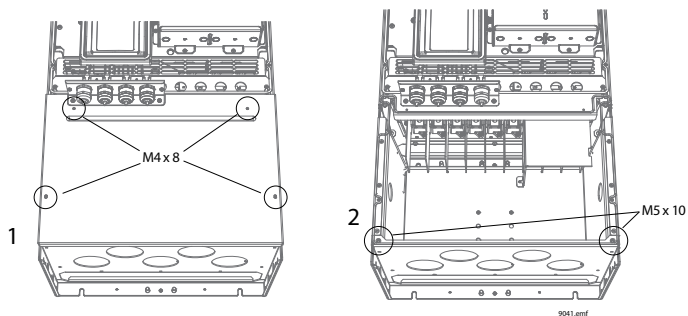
Retirar a tampa dos cabos e a placa de fixação dos cabos (MR9).
